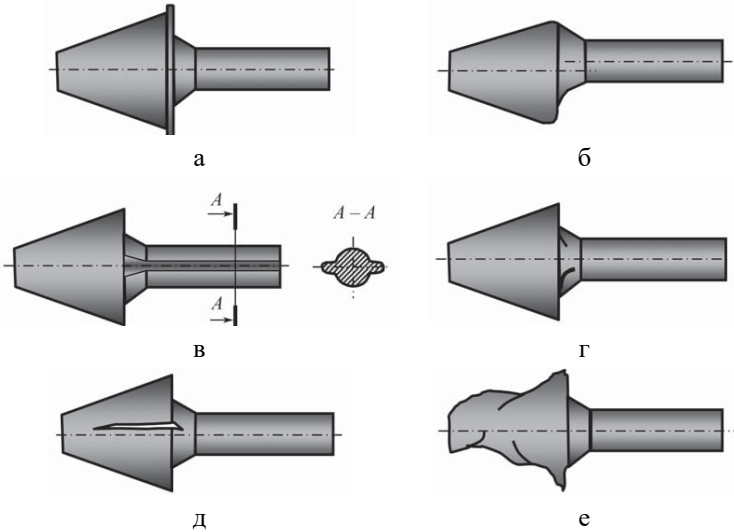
Основні види дефектів під час штампування прутка в складальному струмку ГKM: а – торцевий задилок; б – зміщення осей складального струмка й осі пруткової заготовки; в – задилок за роз’ємом затискних матриць; г – закови в перехідній зоні заготовки; д – тріщина в зоні висаджування заготовки; е – втрата стійкості висаджуваної частини заготовки
